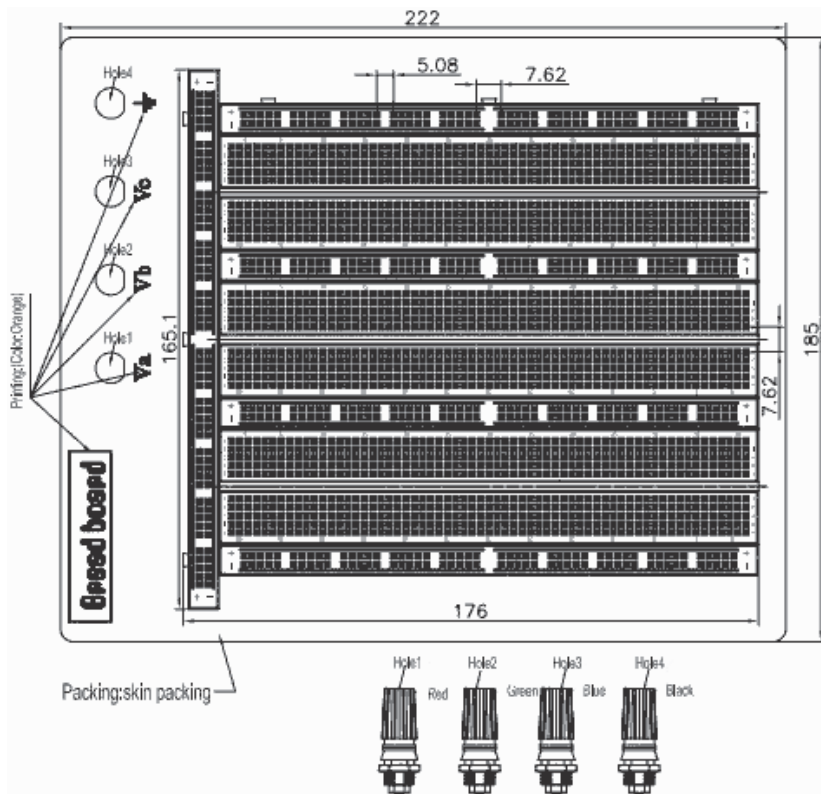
Внешний вид макетной платы BB-3T5D+J
